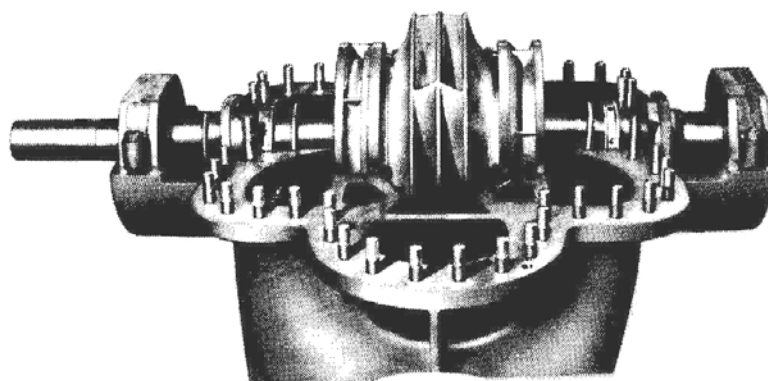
Bomba com o corpo superior removido, disponível para inspeção
